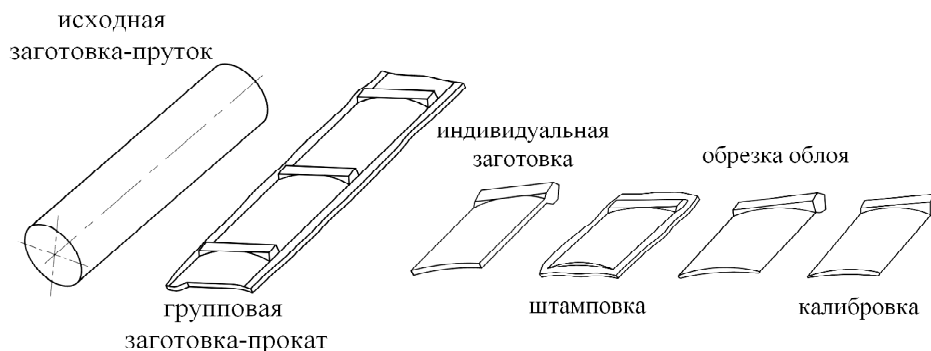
Последовательность технологических переходов точной горячей штамповки рабочих лопаток компрессора из прутка
